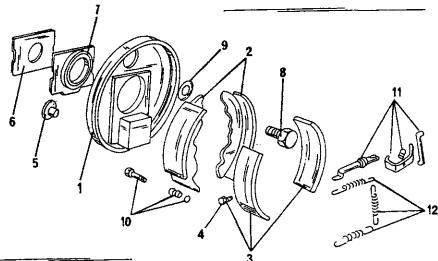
Монтажный чертеж тормоза заднего колеса Girling.
